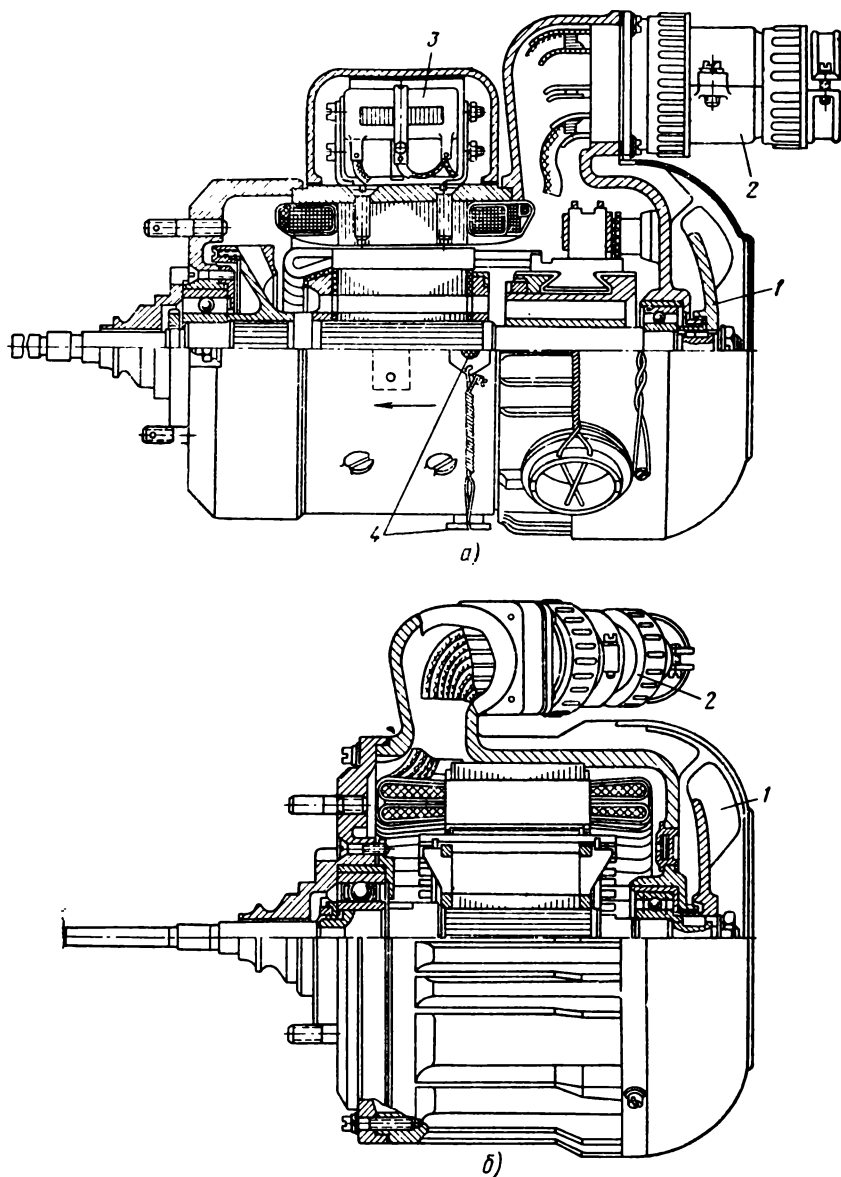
Типовая конструкция двигателя для привода внебакового ЭЦН:
